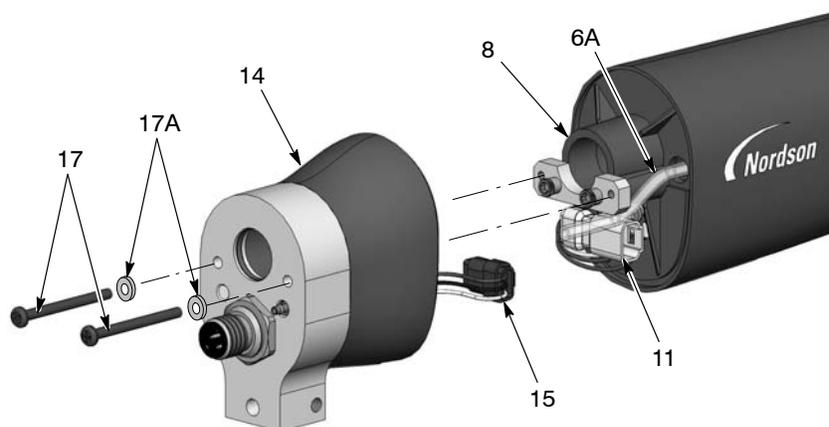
Распылитель для монтажа на штанге, разборка, 1 из 3
